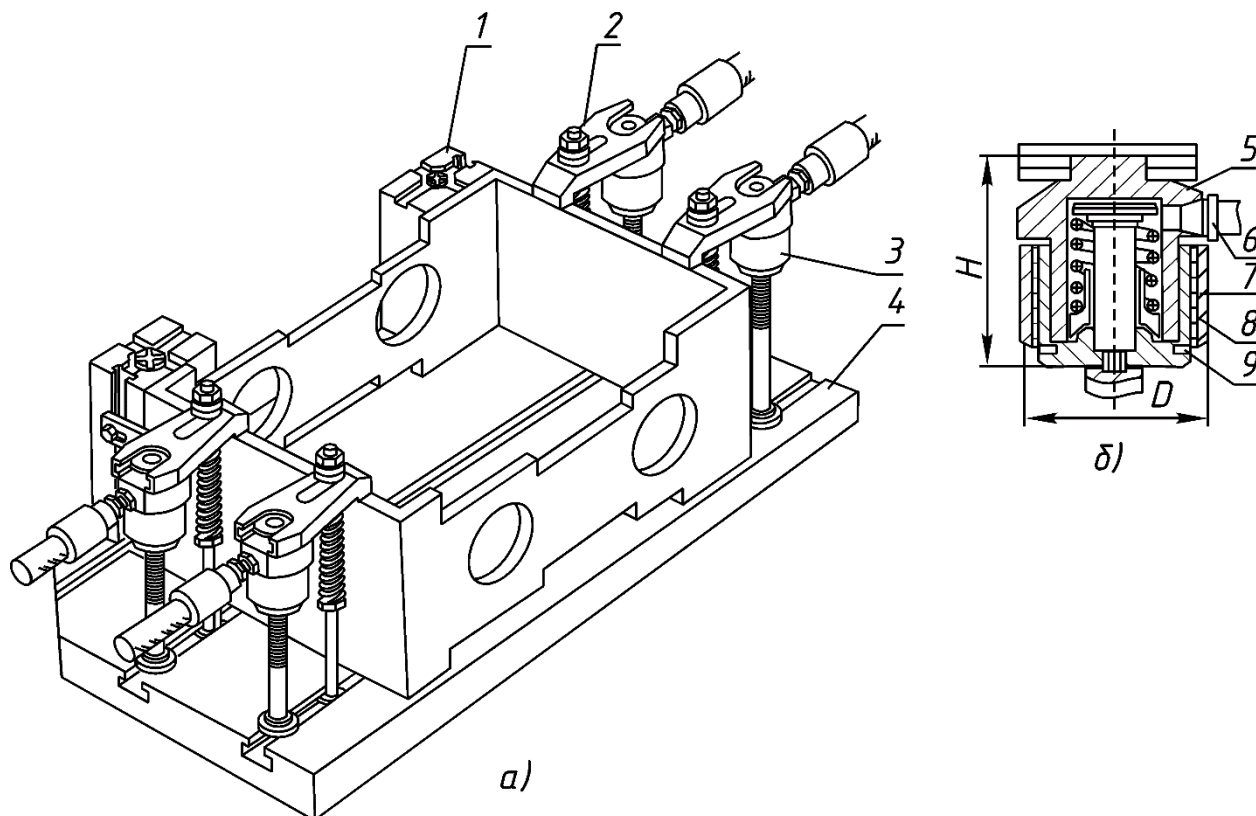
Приспособление из элементов АСП–ЧПУ: а) общая компоновка; б) гидроцилиндр прихвата. 1 – корпусные элементы-упоры для базирования заготовки
